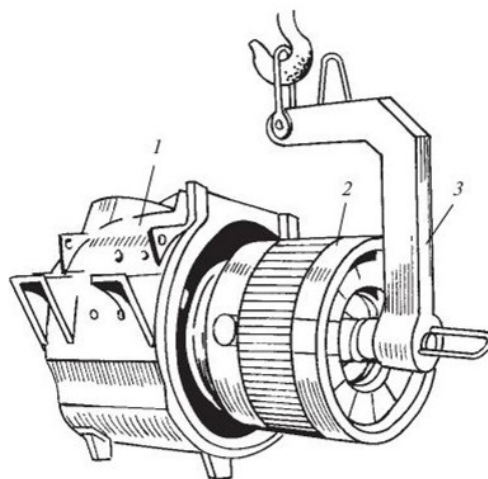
Схема извлечения якоря двигателя с помощью скобы
